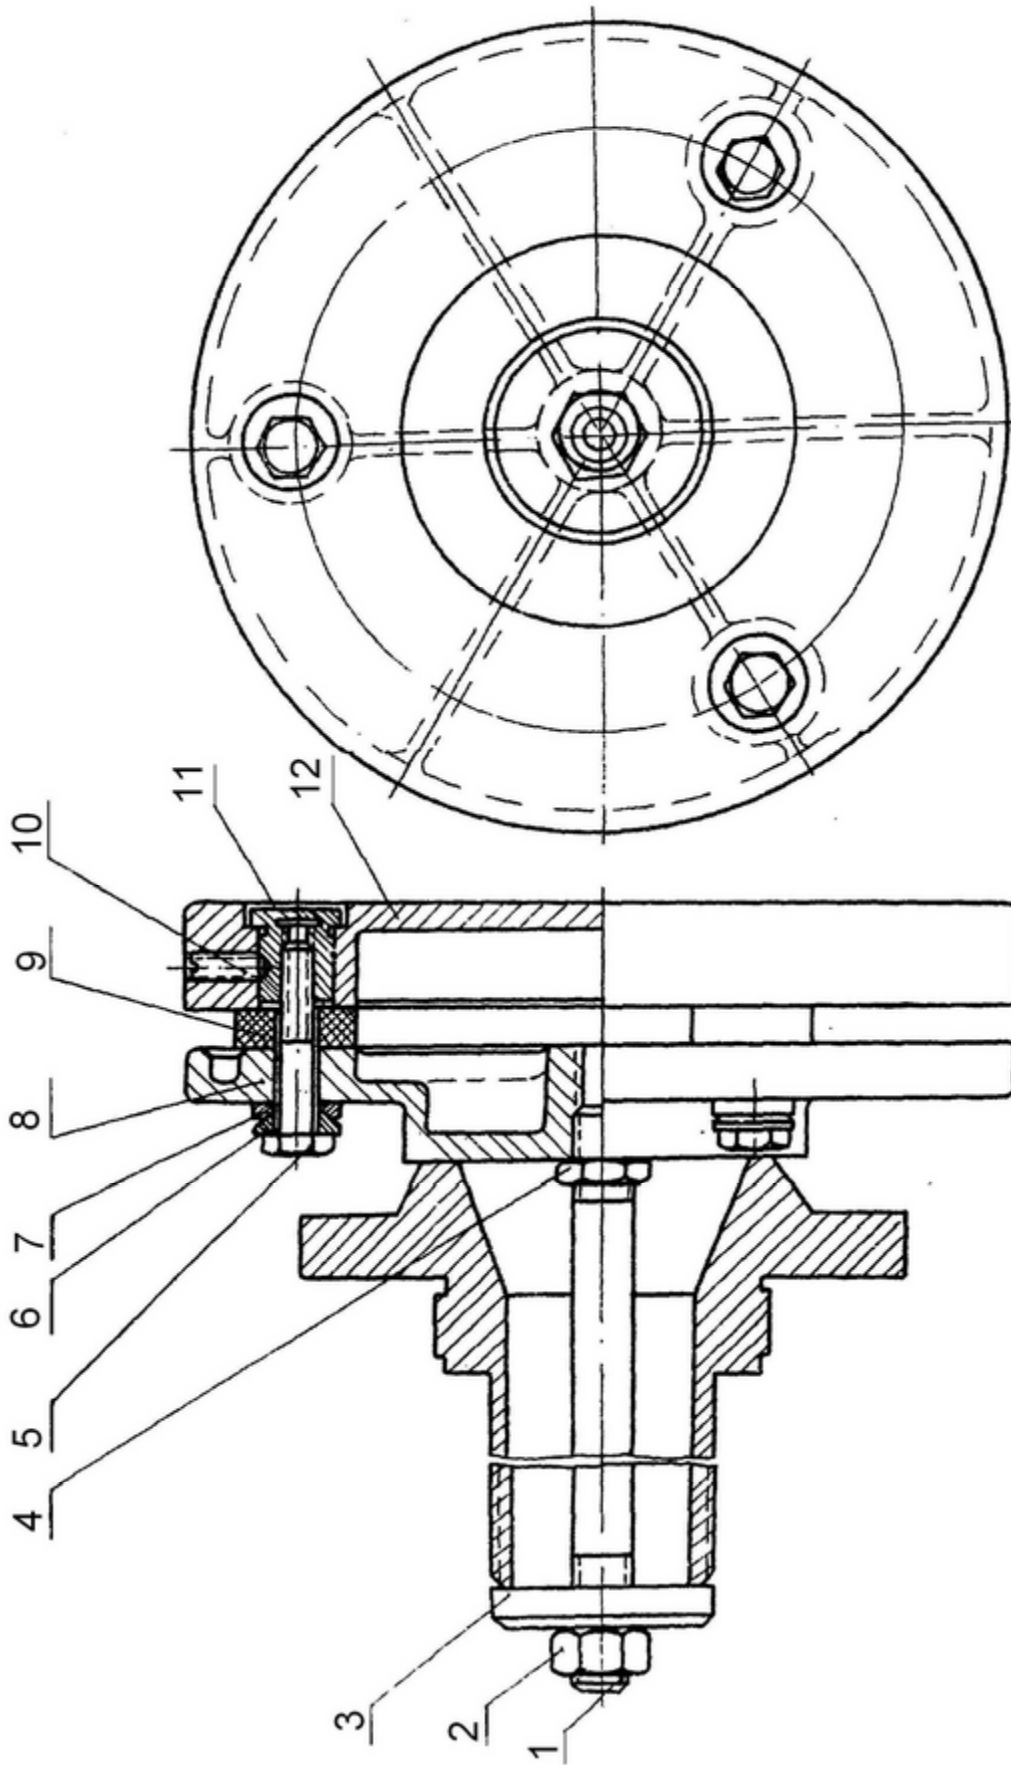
Приспособление для проверки перпендикулярности оси шпинделя к поперечному суппорту револьверных станков СД 8532 – 4006
